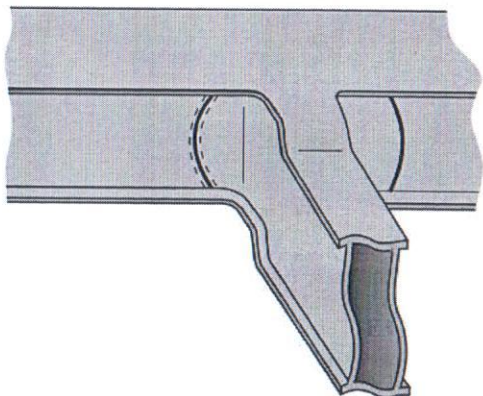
Контроль околошовной зоны сварного соединения на вертикальных стенках в переходе от продольной балки к поперечной
